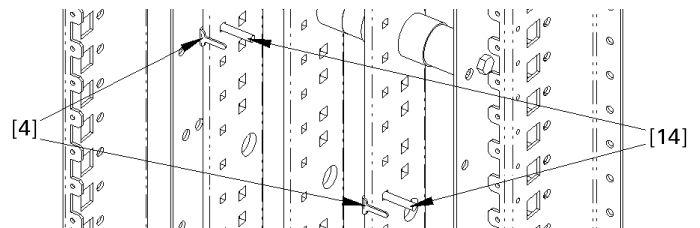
Vue isométrique de l'installation des assemblages de boulons de carrosserie sur les phases A et C.
